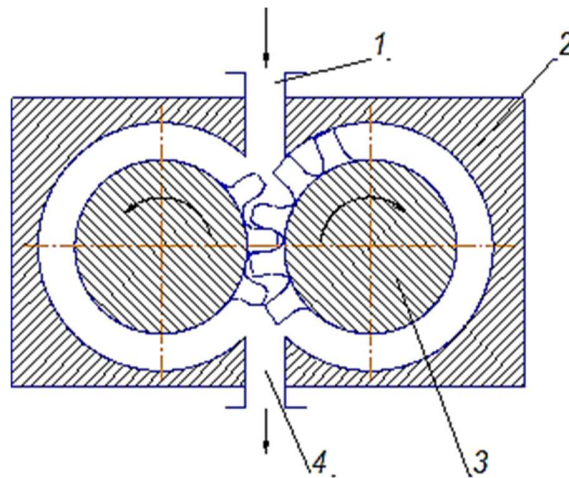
Схема шестеренного насоса: 1 – вхідний патрубок; 2 – корпус; 3 – шестерні, що обертаються назустріч одна одній; 4 – вихідний патрубок
